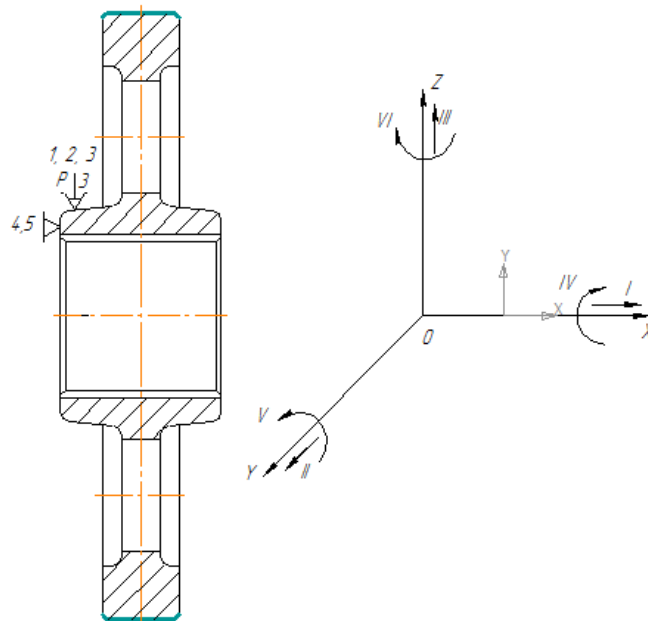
Схема базування заготовки у трьохкулачковому патроні
